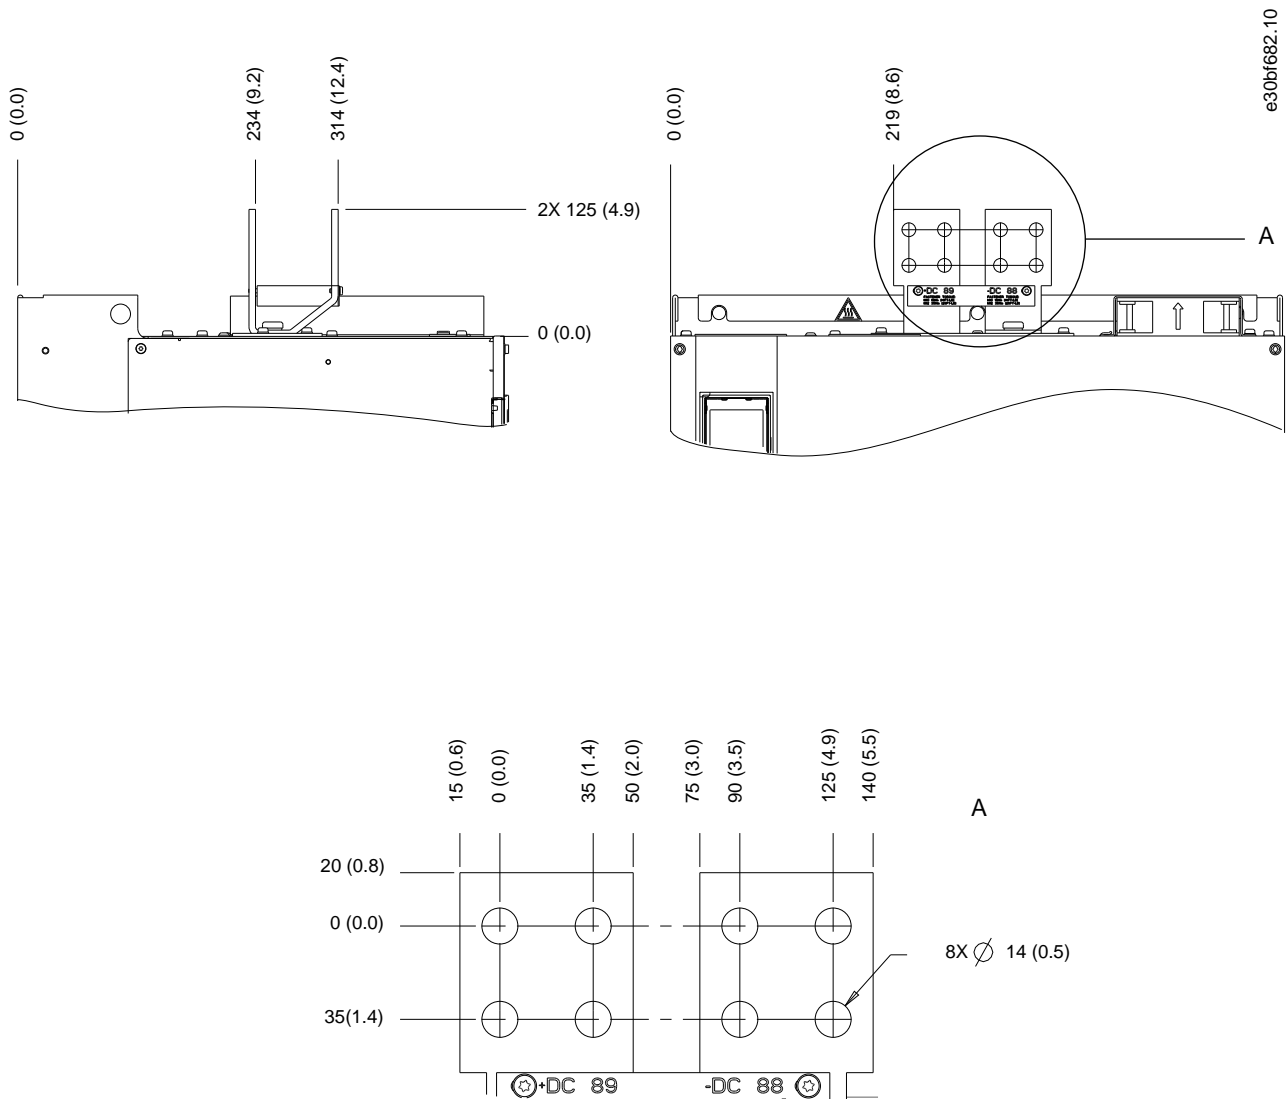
Dimensions des bornes de répartition de la charge/régén. E4h (vues latérales)
